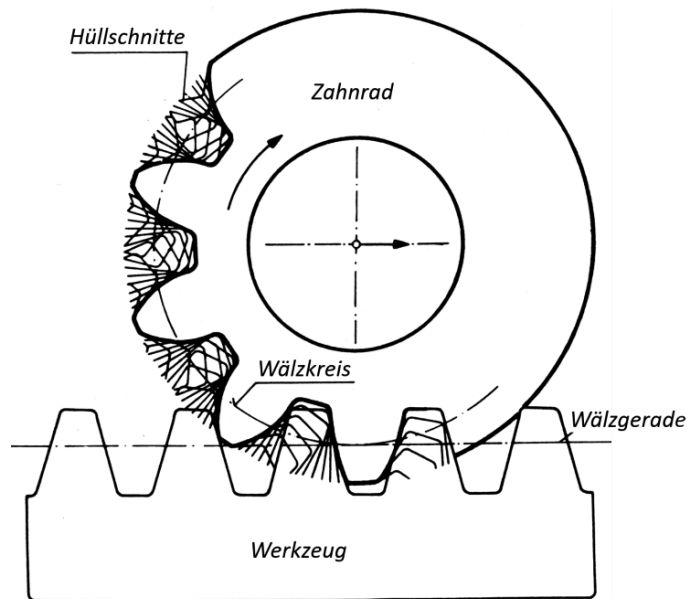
/8 Entstehung der Zahnflanken aus den Hüllschnitten beim Abwälzen eines zahnstangenförmigen Werkzeugs
